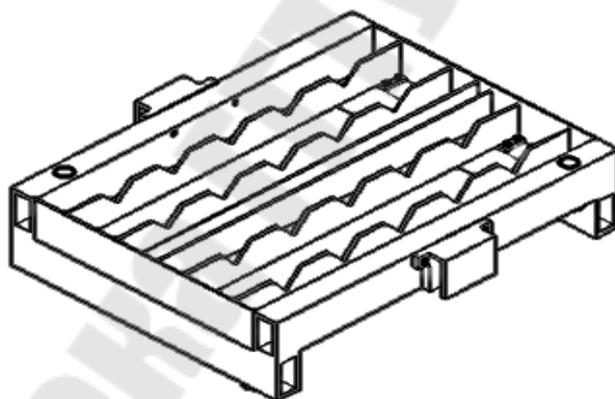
Поддон для укладки заготовок и готовых деталей
